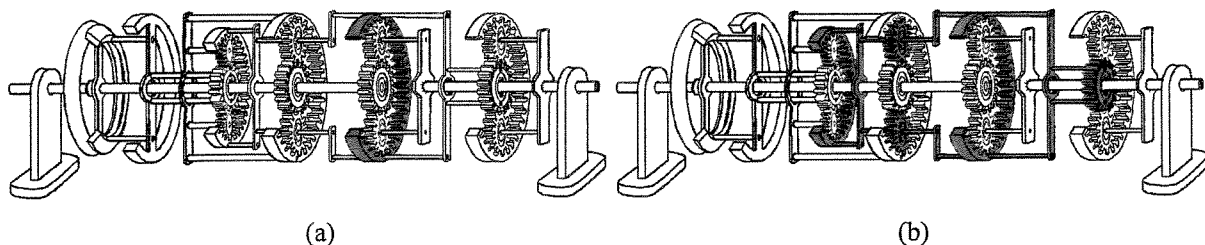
(a) Engrenagem anular do planetário 1 (destaque); (b) Elementos de mesma velocidade da engrenagem destacada.
